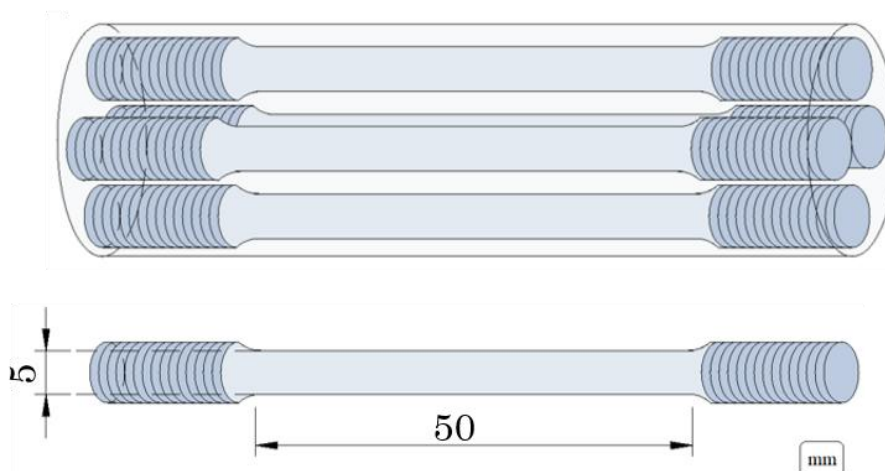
Esquema de las probetas cilíndricas para ensayos de tracción simple, orientadas paralelamente al eje longitudinal de las barras
